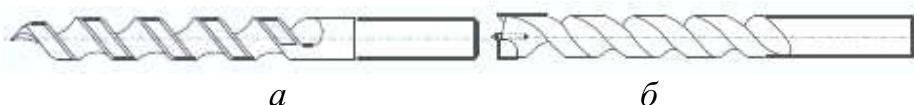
Сверла для сверления сквозных отверстий: без направляющей ленточки (а) и с направляющей ленточкой (б)
